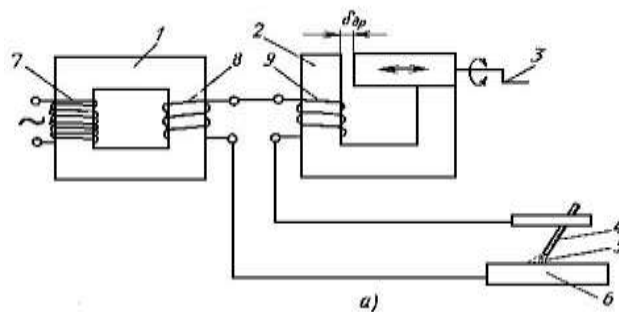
Схема сварочного поста трансформатора СТЭ
